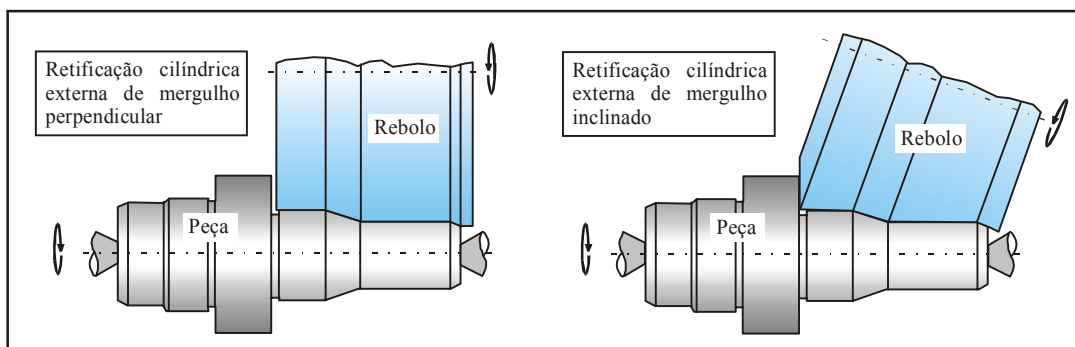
Retificação cilíndrica externa de mergulho perpendicular e inclinado, entre pontas [15].
